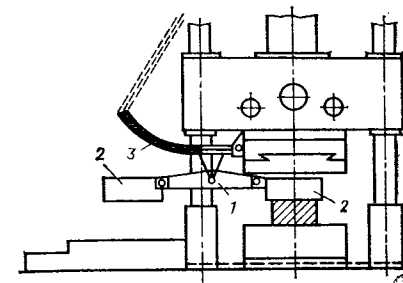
Разрубка топором с противовесом: 1 — державка; 2 — топоры; 3 — моно-рыльс
